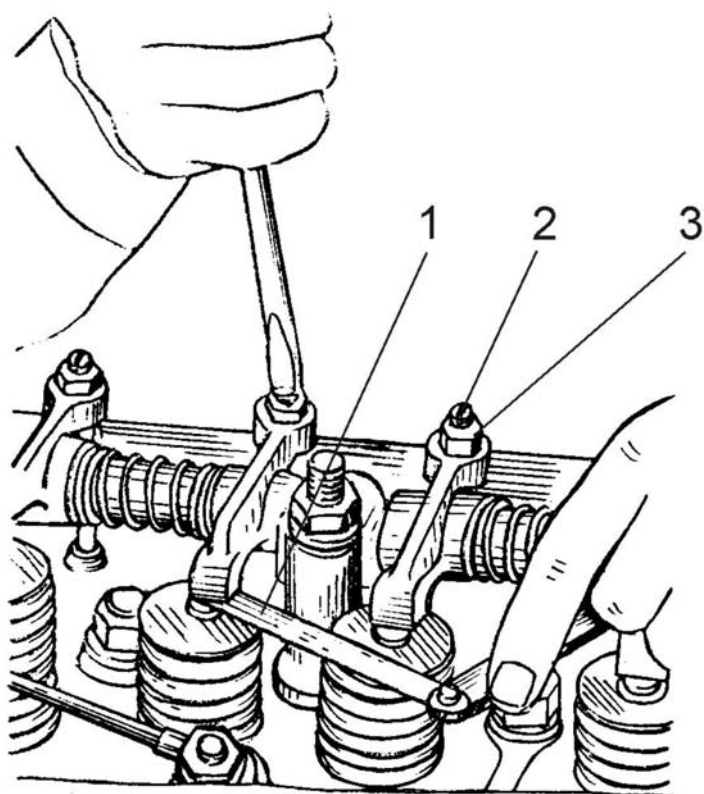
Проверка и регулировка зазора между клапанами и коромыслами
